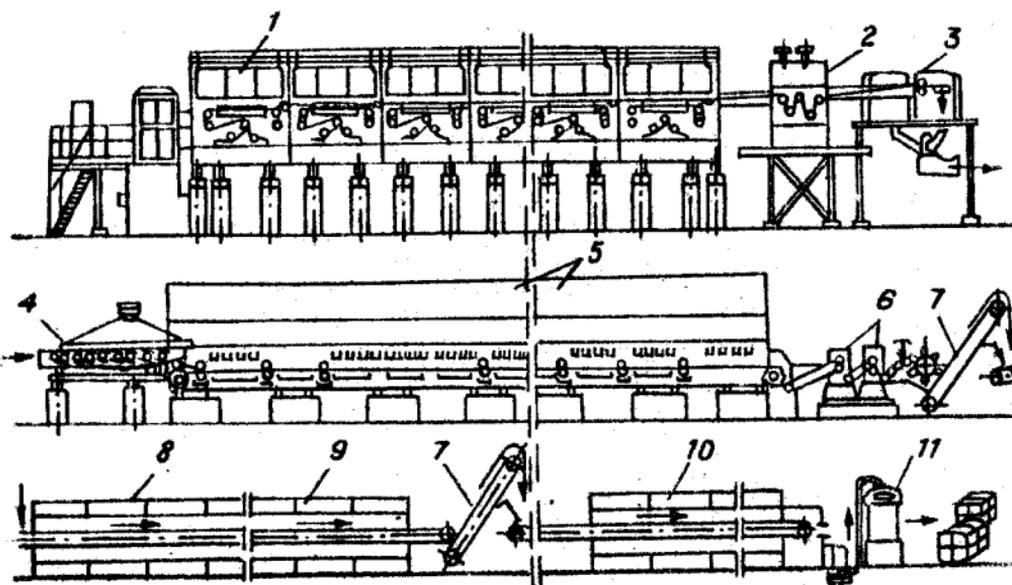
Схема агрегата ША-25-ИР: 1 - прядильная машина; 2 - тянущие вальцы; 3 - режательная машина; 4 - аппарат для стгонки сероуглерода; 5 - отделочные машины; 6 - отжимные валы; 7 - рыхлитель; 8 и 9 - сушилки; 10 - камера кондиционирования; 11 - упаковочный пресс.
